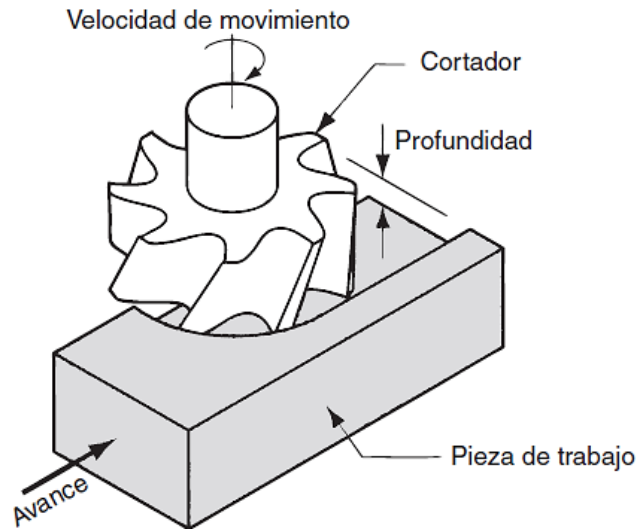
Proceso de fresado frontal, tomada de [37].
